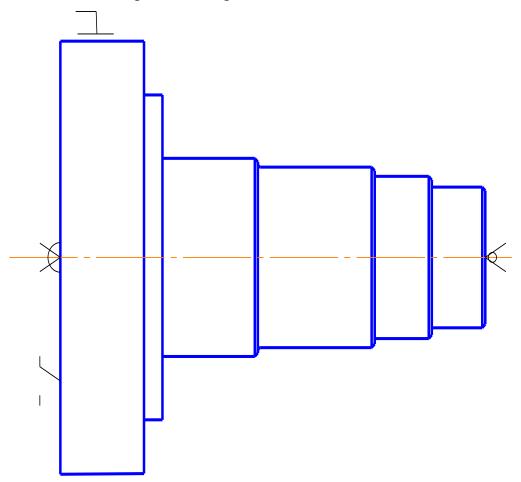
Эскиз базирования детали на токарной операции
